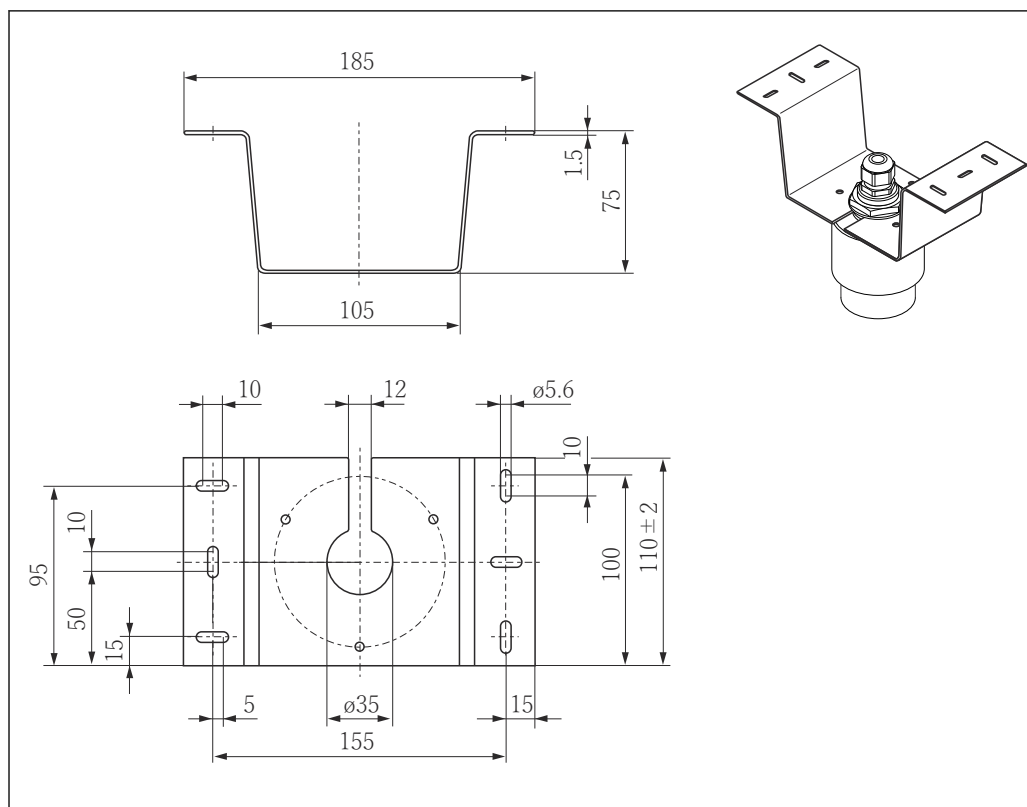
Dimensiones del soporte para montaje en techo. Unidad de medida mm (in)
